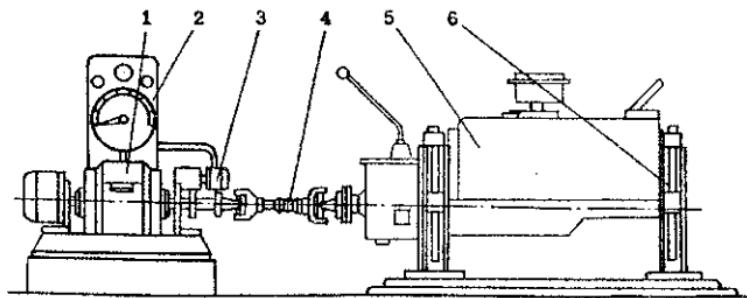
Стенд для обкатки и испытания двигателей:
